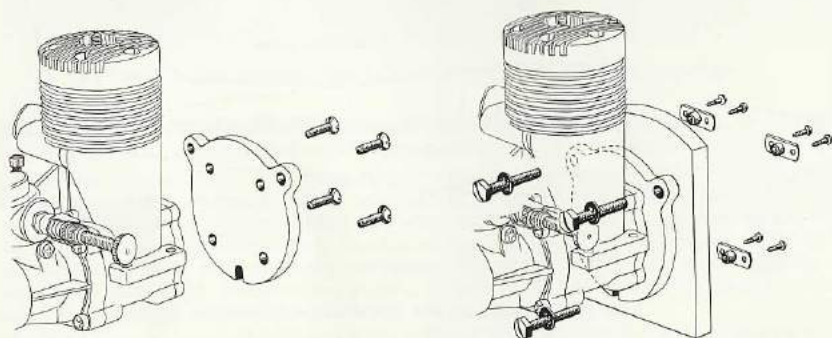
Erläuterung zum Motoranbau. Hier wird ein Motor in senkrechter Lage befestigt.
